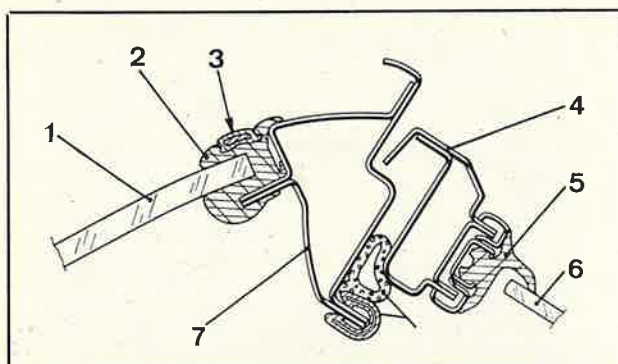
Vue en coupe du pare-brise du pied avant droit et de la porte.
